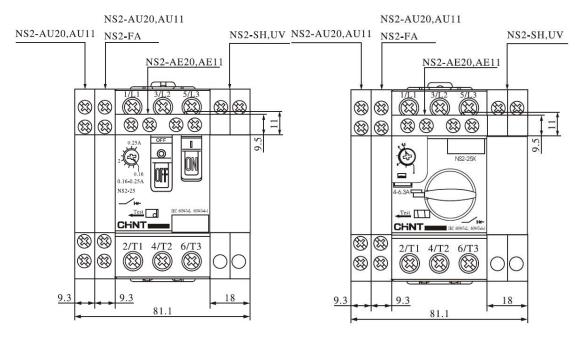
Положения сборки и габаритные размеры вспомогательного оборудования
